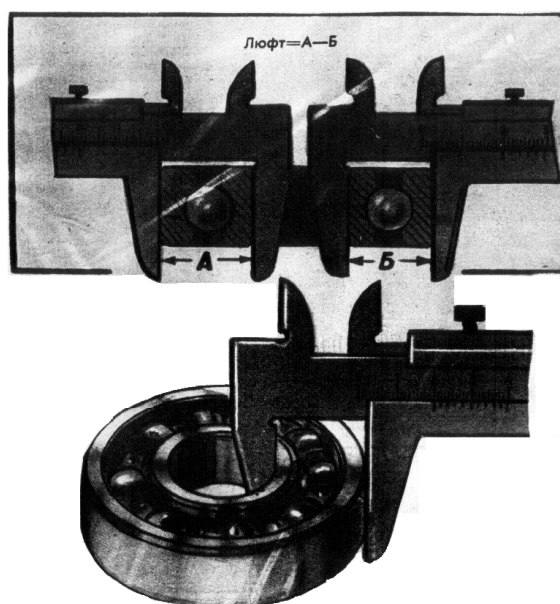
Схема измерения радиального зазора подшипника штангенциркулем.
